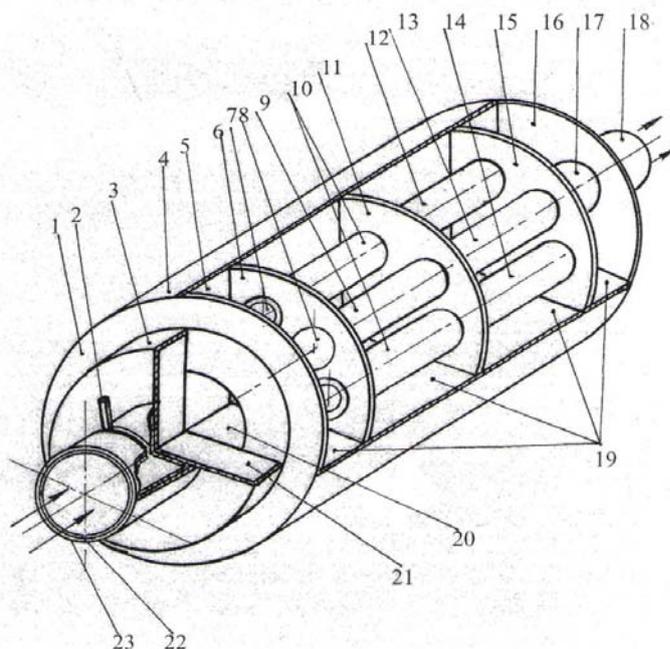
Многоступенчатый фильтр для очистки отработавших газов дизеля от твердых частиц. 1,16 - торцевые стенки; 2 - поворотный рычаг; 3 - коллектор газораспределения; 4 - корпус; 5, 19 - продольные перегородки; 6, 11, 15 - поперечные перегородки; 7 - отверстие; 8 - глухая стенка; 9 - фильтр второй ступени; 10 - фильтры первой ступени; 12, 14 - фильтры четвертой ступени; 13 - фильтр третьей ступени; 17 - отверстие; 18 - выпускной патрубок; 20 - окно; 21 - разделительная переборка; 22 - внутренняя поворотная труба; 23 - внешняя труба подвода газов.
